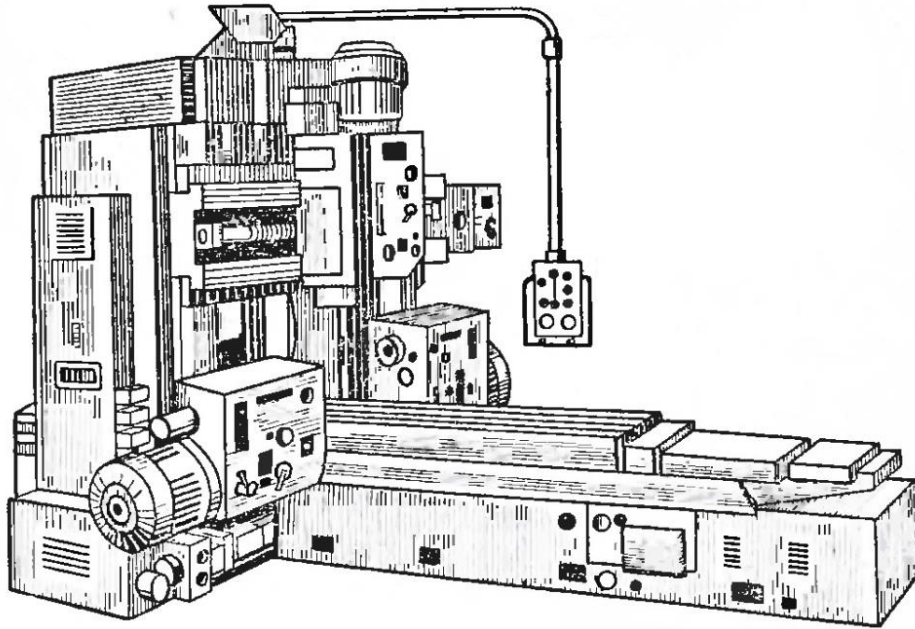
Двостійковий поздовжньо-фрезерний верстат
